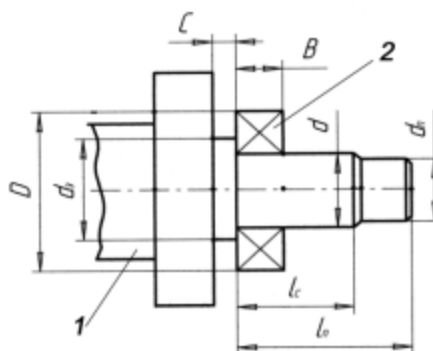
Схема підшипникового знімачів: 1- вал; 2- підшипник
